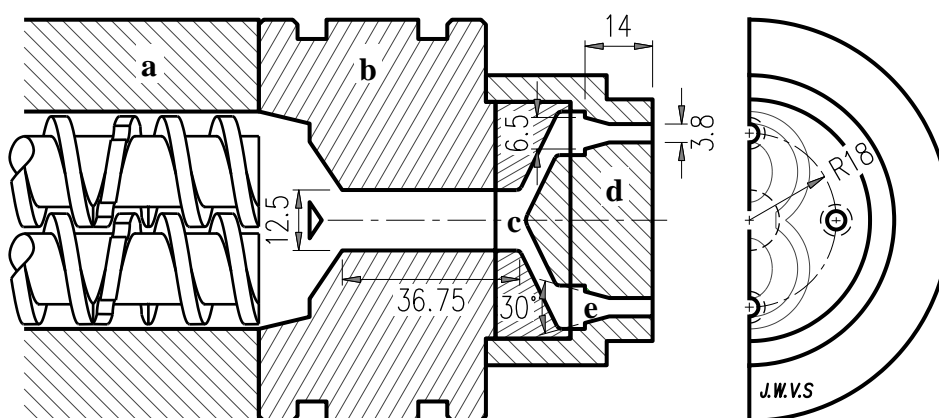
Vista superior em secção transversal do conjunto da placa frontal (matriz) do extrusor Clextral Evolum HT25: (a) cilindro; (b) placa central coletora; (c) placa distribuidora; (d) placa porta-insertos; e (e) furo do inserto. Dimensões em mm.
